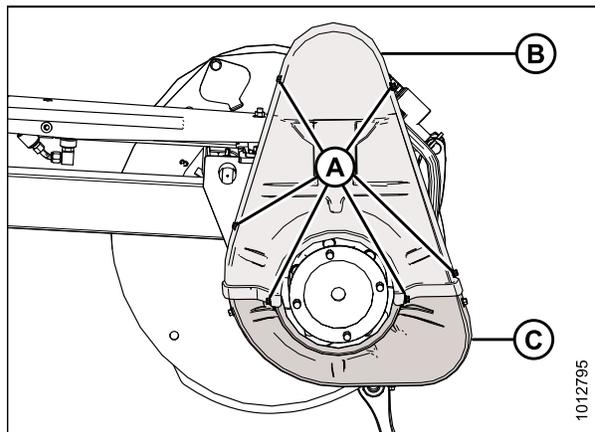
Крышка привода — сдвоенное мотовило
